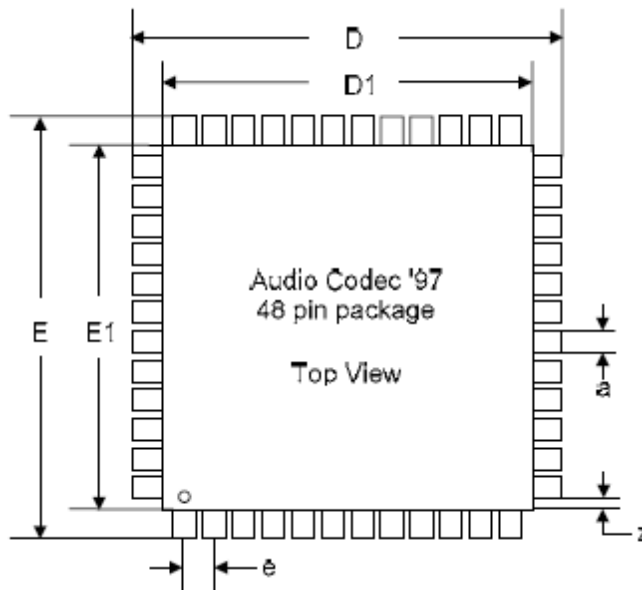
Размеры 48-ми выводного корпуса AC '97
